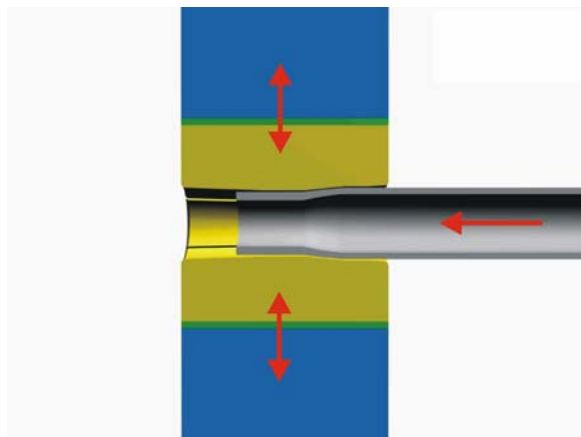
Vorschubkneten ohne Innenwerkzeug
